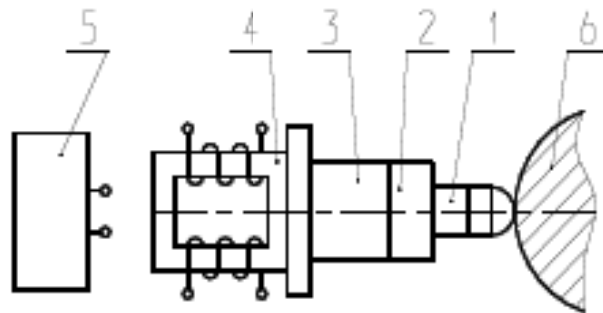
Схема ультразвукової установки з деформуючим інструментом у вигляді напівсфери: 1 – інструмент, що деформує; 2 – концентратор УЗК; 3 – хвилевід; 4 – перетворювач УЗК; 5 – генератор; 6 - оброблювана деталь.
